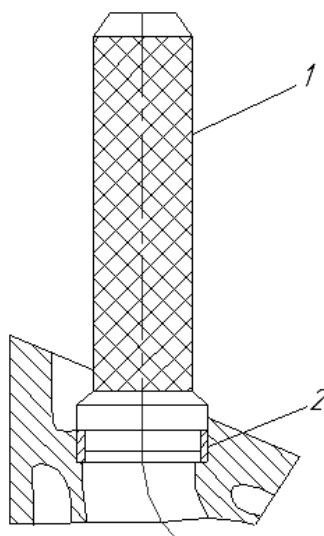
Запрессовка седла клапана (2) с помощью оправки (1)
